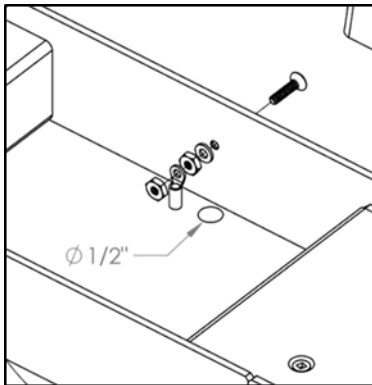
Assemblage du connecteur et trou de passage du fil d'alimentation des rails
